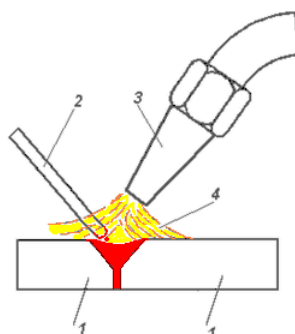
Схема газовой сварки: 1 – основной материал; 2 – присадочный материал; 3 – сварочная горелка; 4 – газовое пламя
